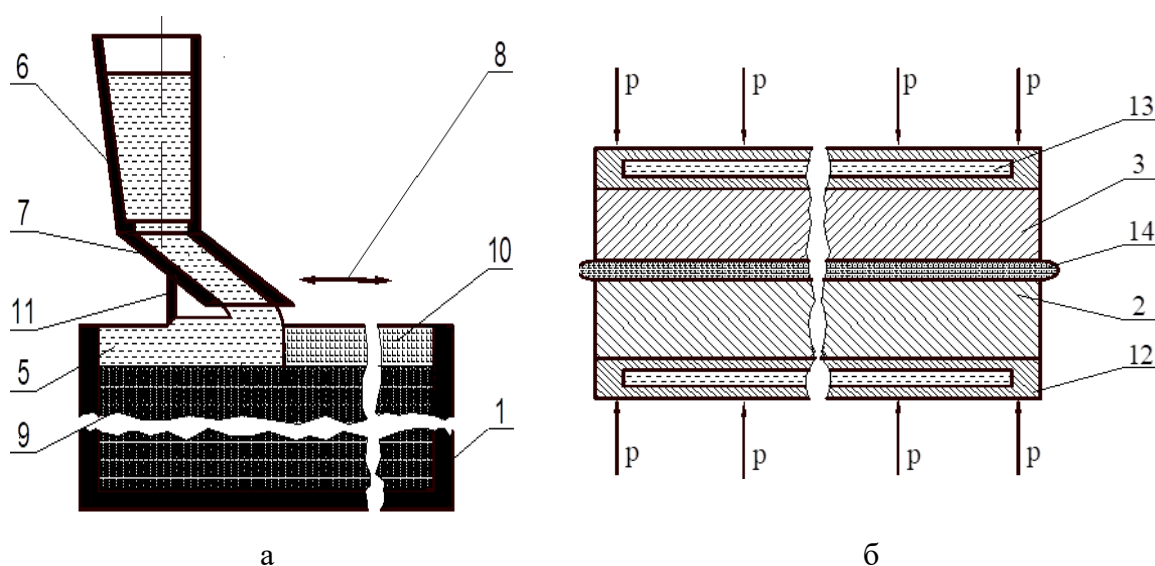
Пристрій для заливки прошарку розплаву між вертикально встановленими пластинами біметалу (а) та пристрій для стискування пластин біметалу (б)
